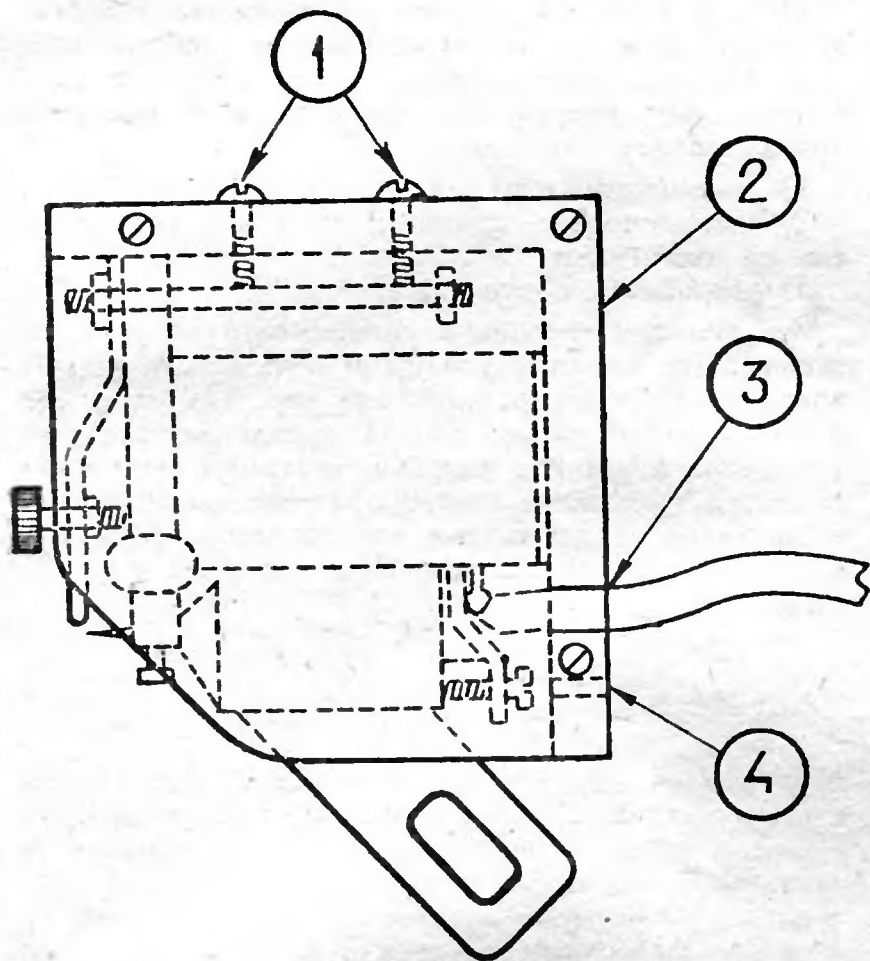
1—винты крепления свинцовой крышки, служащей добавочным грузом. 2—свинцовая крышка. 3—выводной шнур. 4—отверстие для отвертки для натяжки струны крепления якоря
